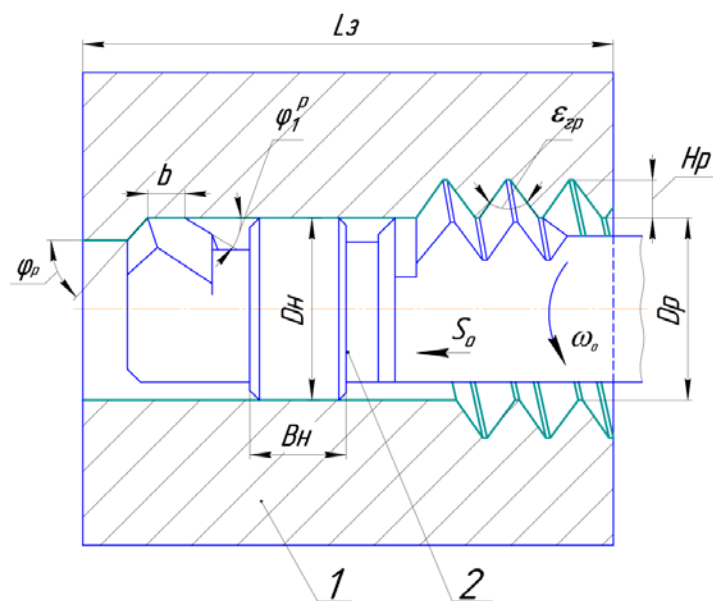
Схема нарезания внутренней резьбы комбинированным инструментом резцом-гребёнкой с направляющей
